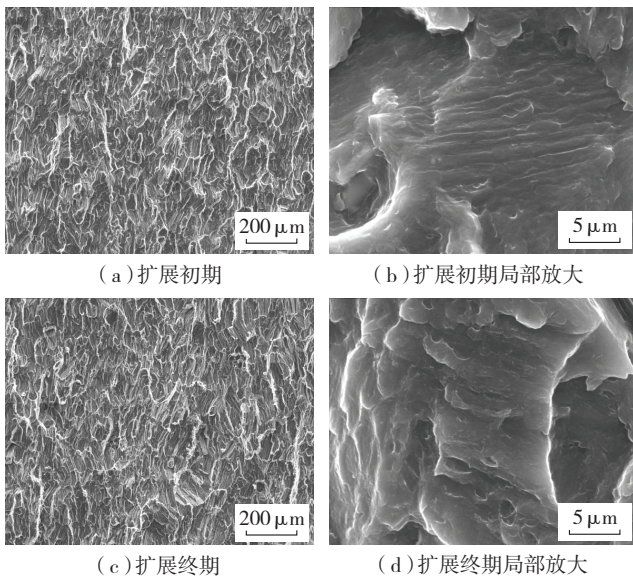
AZ31B镁合金电子束焊接接头HAZ疲劳裂纹扩展断口
